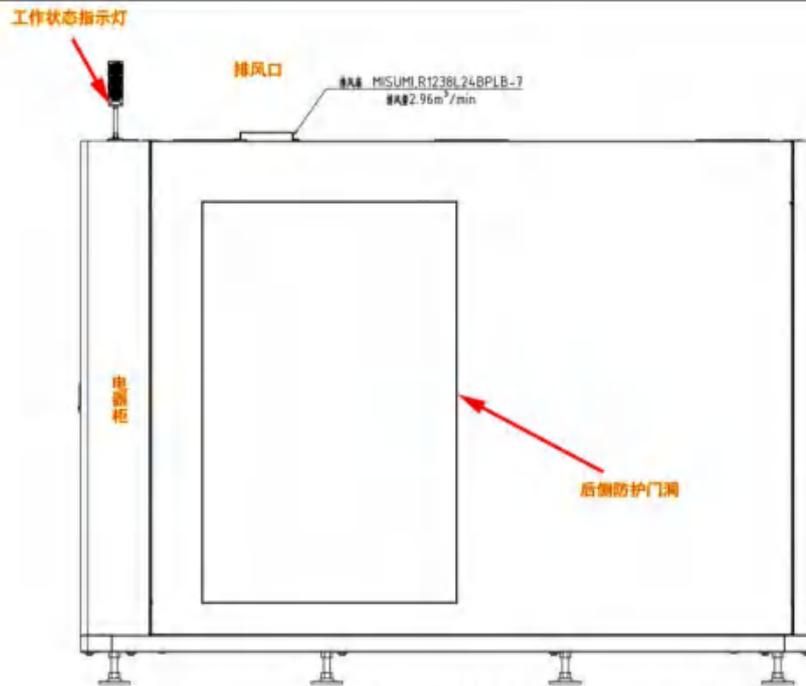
(c) 工业 CT 剖面图 (b-b 剖面)
